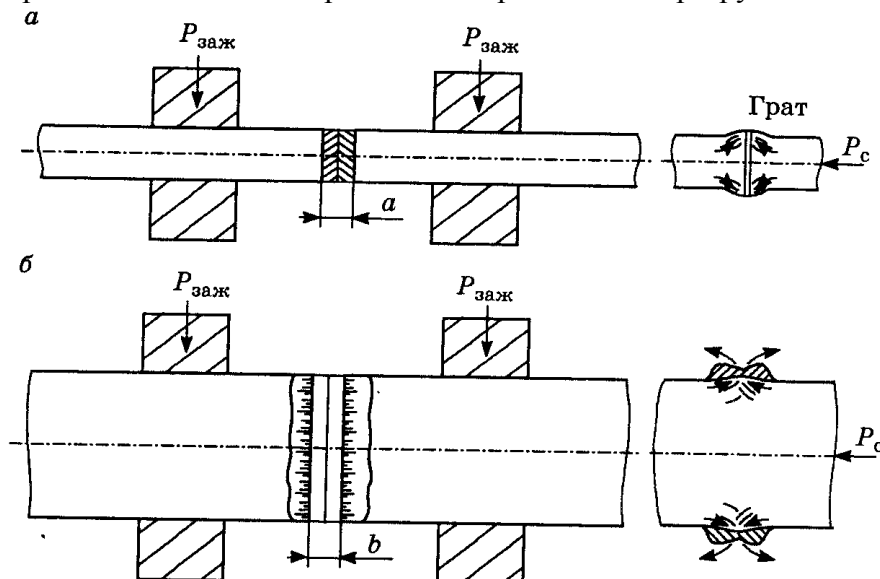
Схемы процесса стыковой сварки:
